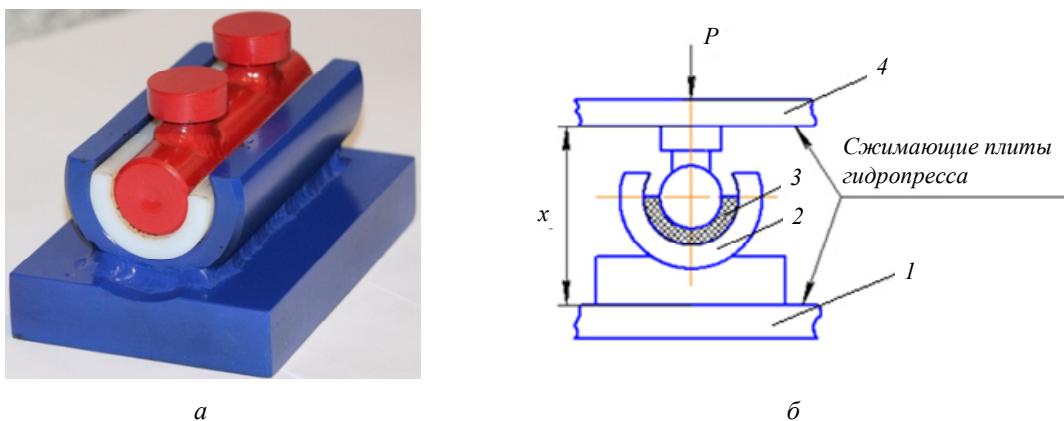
Приспособление для определения коэффициента жёсткости образцов и форма деформации при задаваемой нагрузке: *а* – вид приспособления; *б* – конструктивная схема
